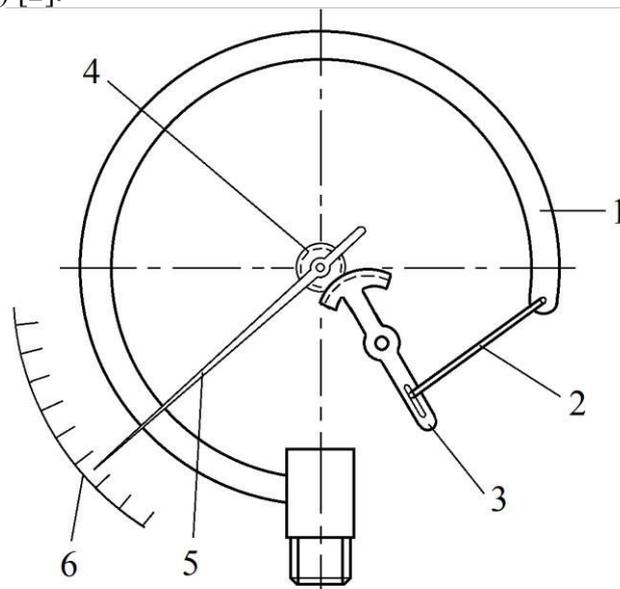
Схема манометра с трубчатой пружиной и передаточным механизмом в виде зубчатого сектора: 1 - трубчатая пружина (трубка Бурдона); 2 – тяга (поводок); 3 - зубчатый сектор; 4 – зубчатое колесо (трибка); 5 – стрелка; 6 - шкала
